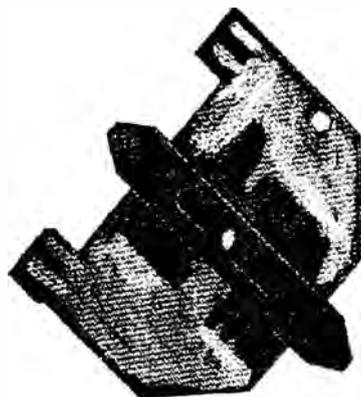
Medidor de soldadura en ángulo y de refuerzo de soldadura
